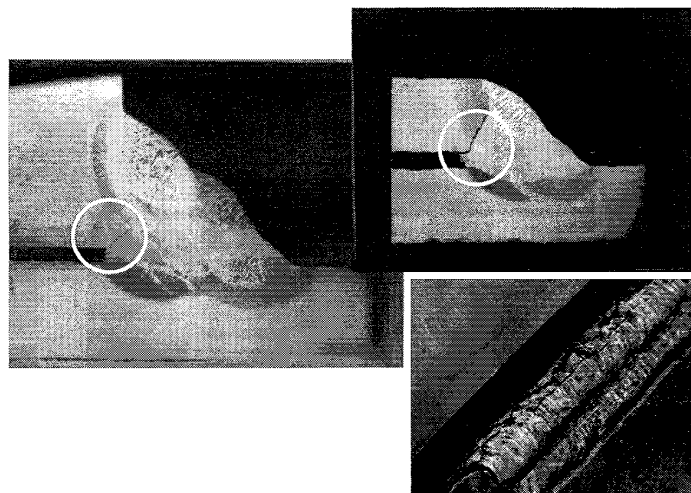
Fissuras em zonas de concentração de tensões
